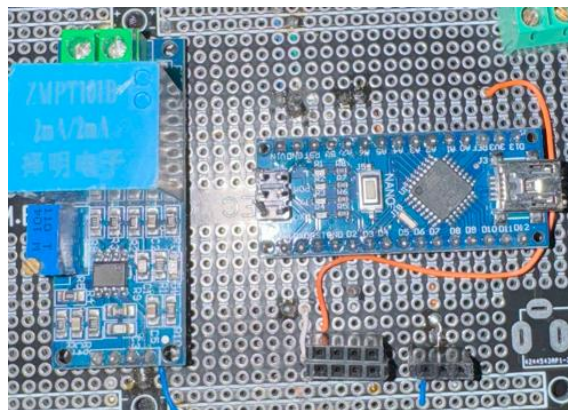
Prototipo de Placa PCB Fuente: Autor
